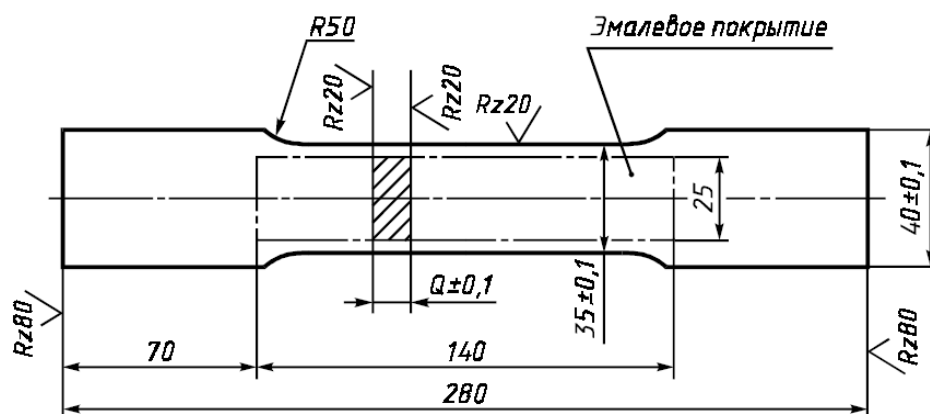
Форма и размеры образца для испытания эмаливого покрытия на растяжение
